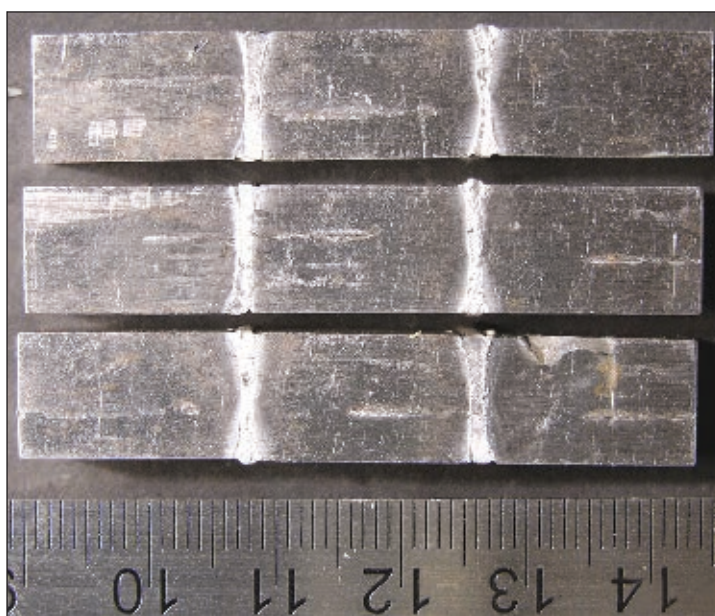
Сечение сварных соединений на боковой поверхности заготовок после разлома
